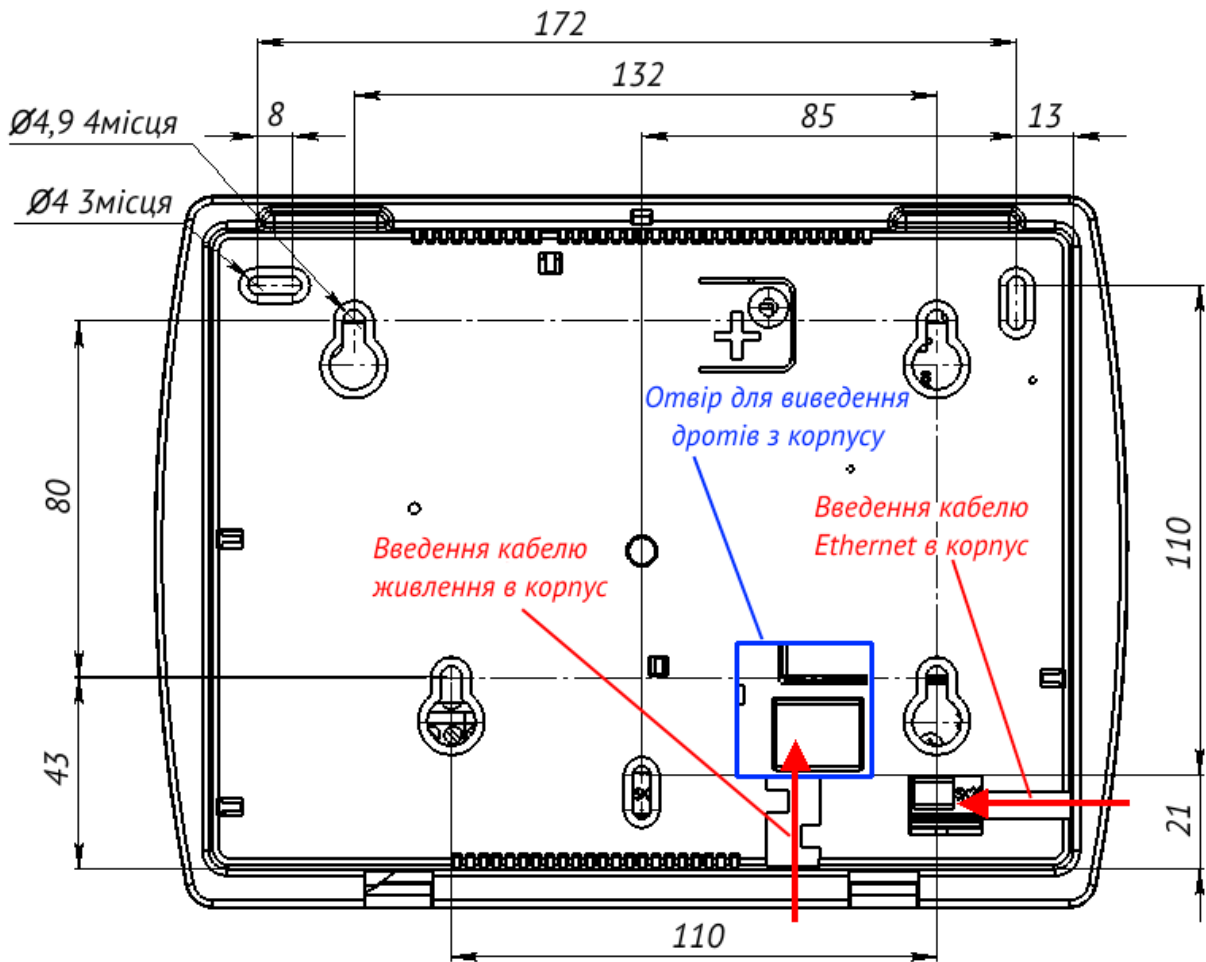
Зовнішній вигляд і габаритні розміри ППКОП
